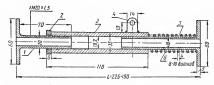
Приспособление для замера расхождения щек коленчатого вала: 1 — неподвижная часть; 2 — контргайна; 3 — свертывающаяся часть; 4 — ушно для индинатора; 5 — трубчатый шток; 6 — пружина.
